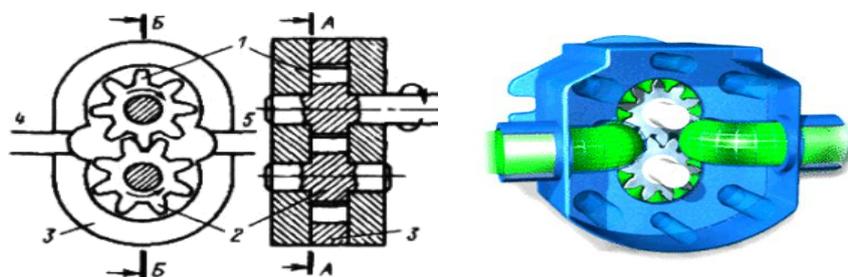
Шестеренный насос: 1,2 – шестерни; 3 – корпус; 4 – всасывающий патрубок; 5 – нагнетательный патрубок
